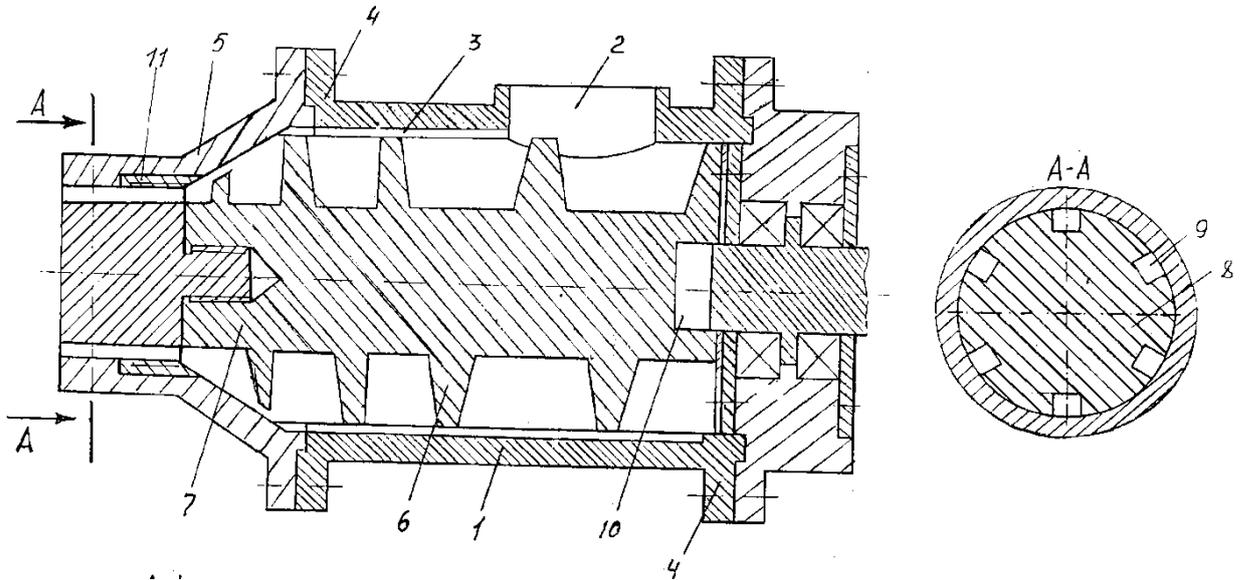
Шнековый пресс-гранулятор: 1 – корпус; 2 – загрузочная горловина; 3 – ребра для измельчения и направления движения кормовой смеси; 4 – фланцы; 5 – кожух гранулятора; 6 – прессующий однозаходный шнек с переменным шагом витков; 7 – вал; 8 – фильера; 9 – продольные пазы; 10 – паз для зацепления с приводом; 11 – сменная втулка
